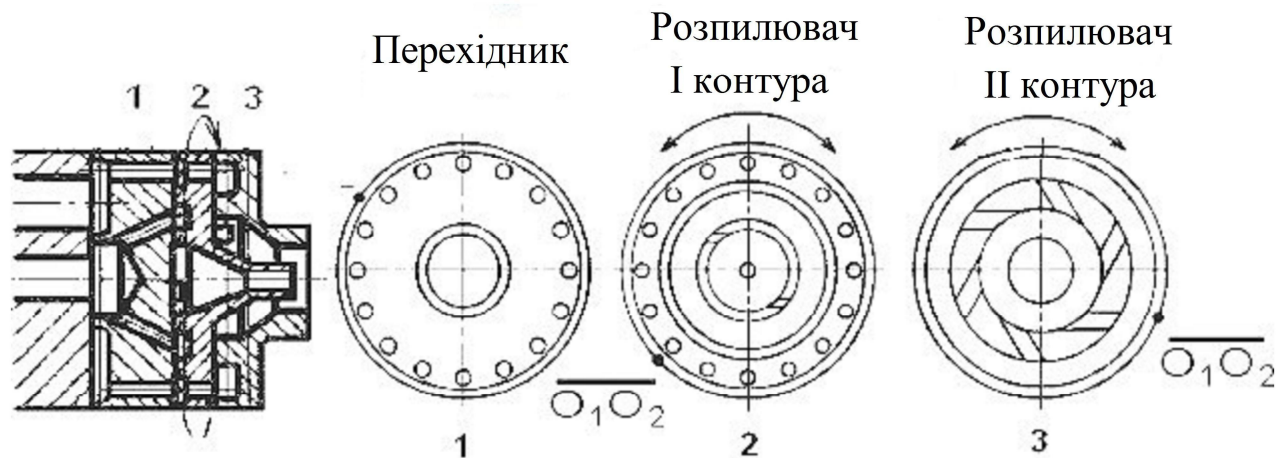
Схема розташування деталей розпилювального пакета з
